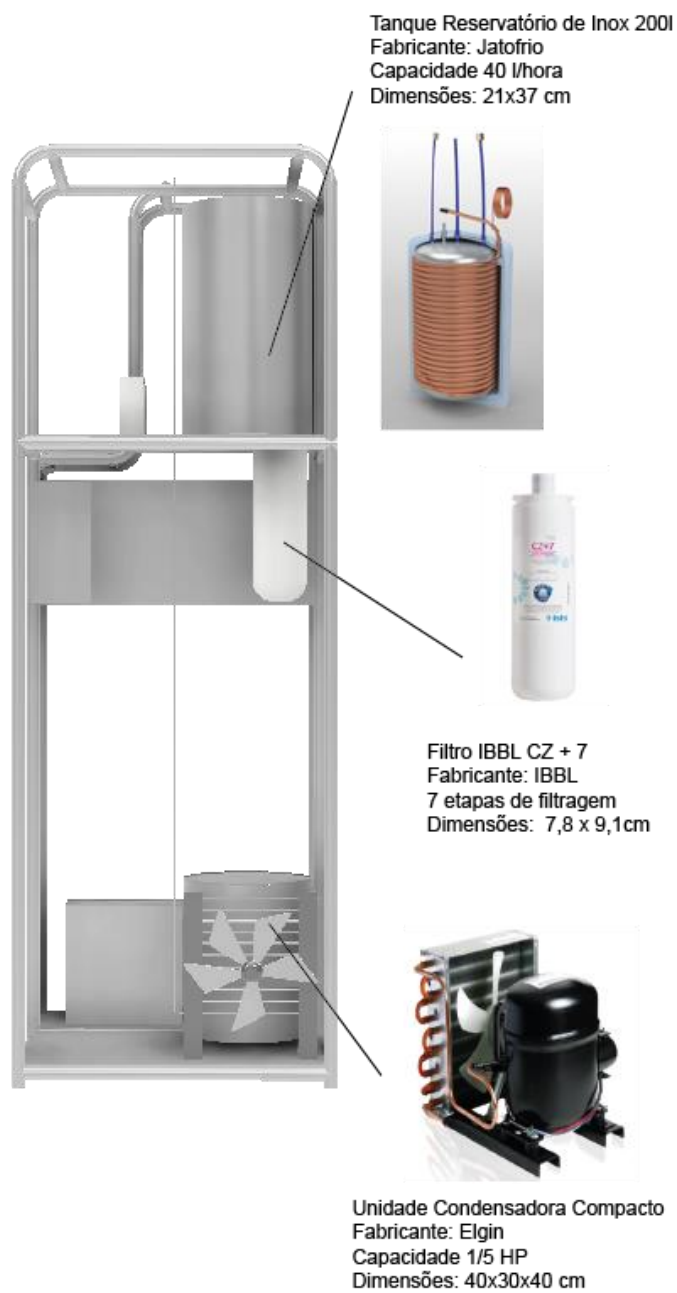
Detalhamento dos Componentes dos Sistemas
